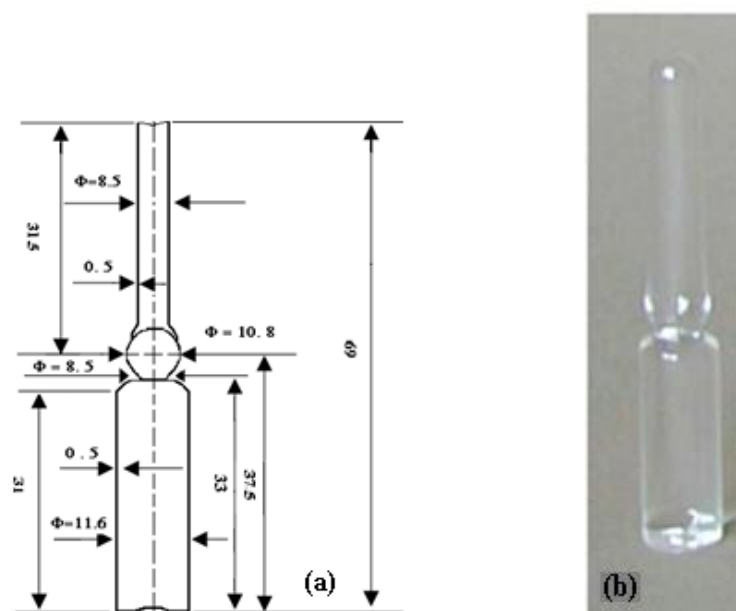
Ampoule utilisée pour contenir la solution dosimétrique : (a) forme et dimensions et (b) photographie.
